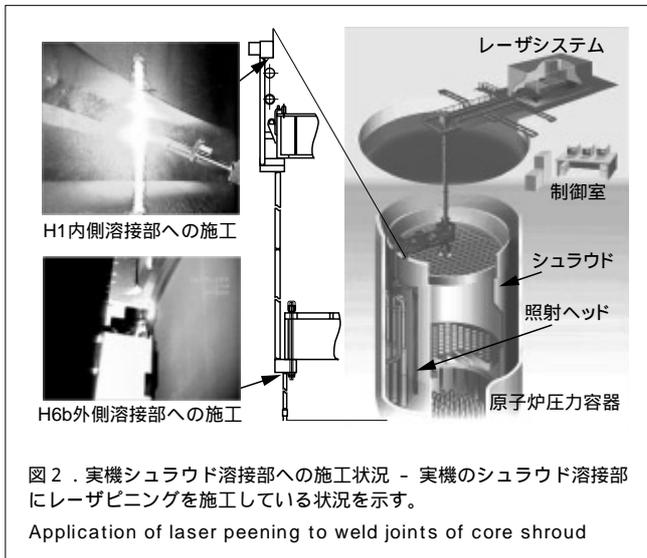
．実機シュラウド溶接部への施工状況 - 実機のシュラウド溶接部にレーザーピーニングを施工している状況を示す。
